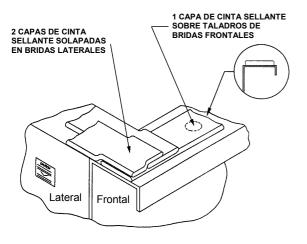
Aplicación de Cinta Sellante en la Sección Inferior
